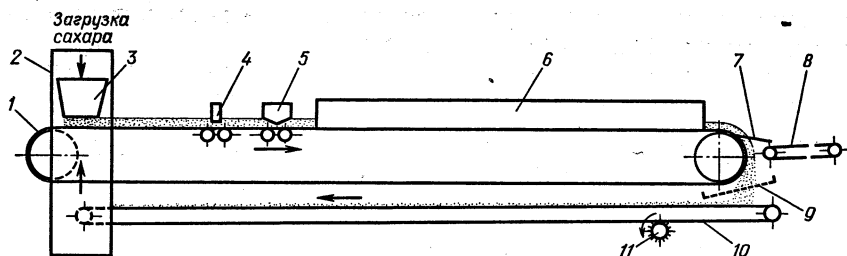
Схема поточной линии производства фруктового пата и цветного горошка отливкой в непрерывно перемещаемый слой сахарного песка:
